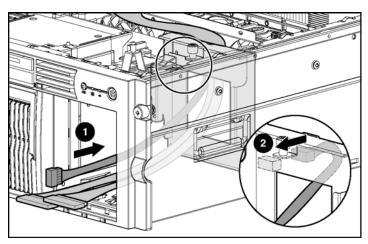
Collegamento e instradamento dei cavi dati e di alimentazione SAS o SATA
